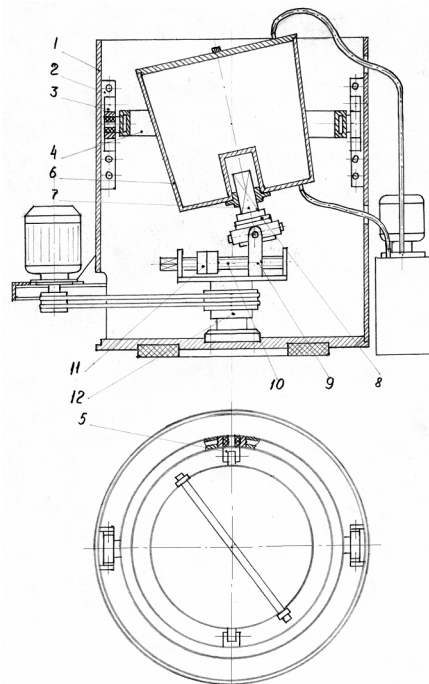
Конструктивна схема вібраційно-відцентрової установки
